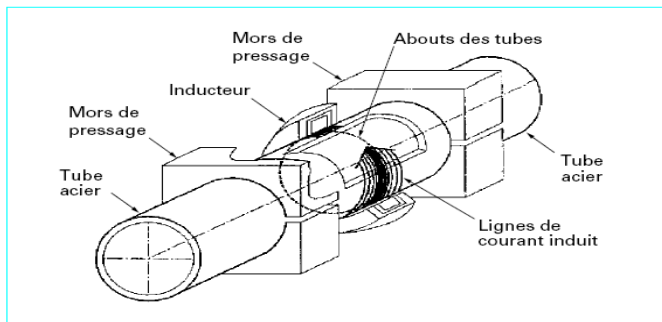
Soudage bout à bout par induction de tubes pour le transport du pétrole
